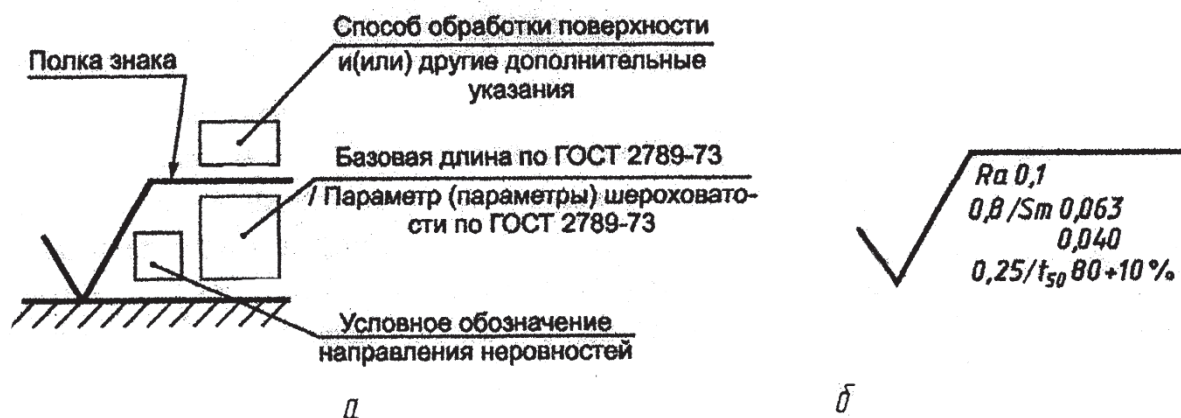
Структура обозначения шероховатости поверхности (а)
